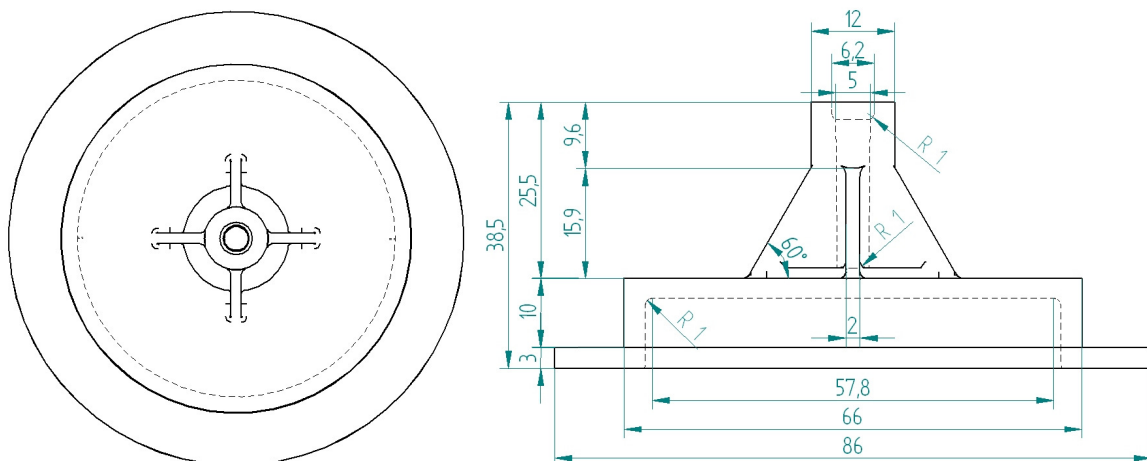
Befestigungsdemonstrator mit 60°-Rippen
